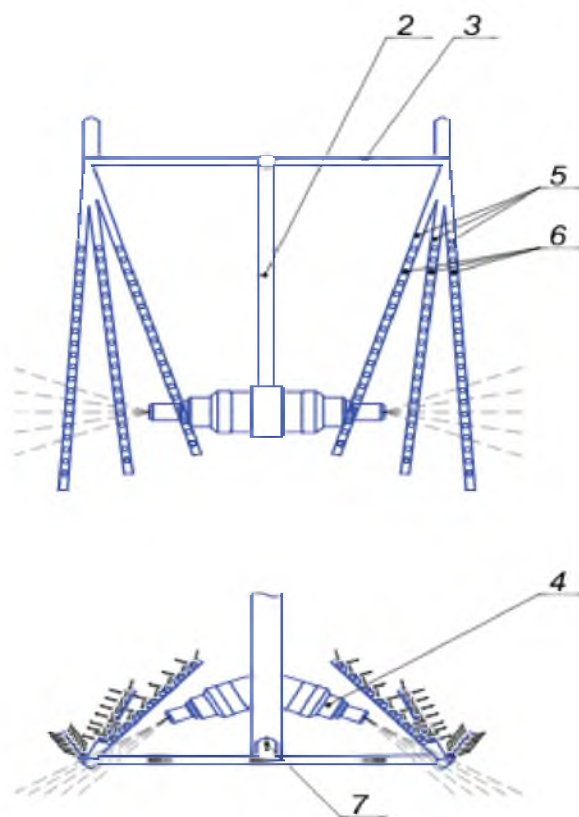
Чертёж пневматического листоподъёмника
